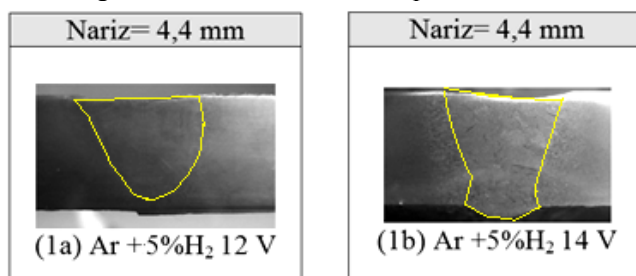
Macrografias de soldas obtidas com 12 e 14 V.
